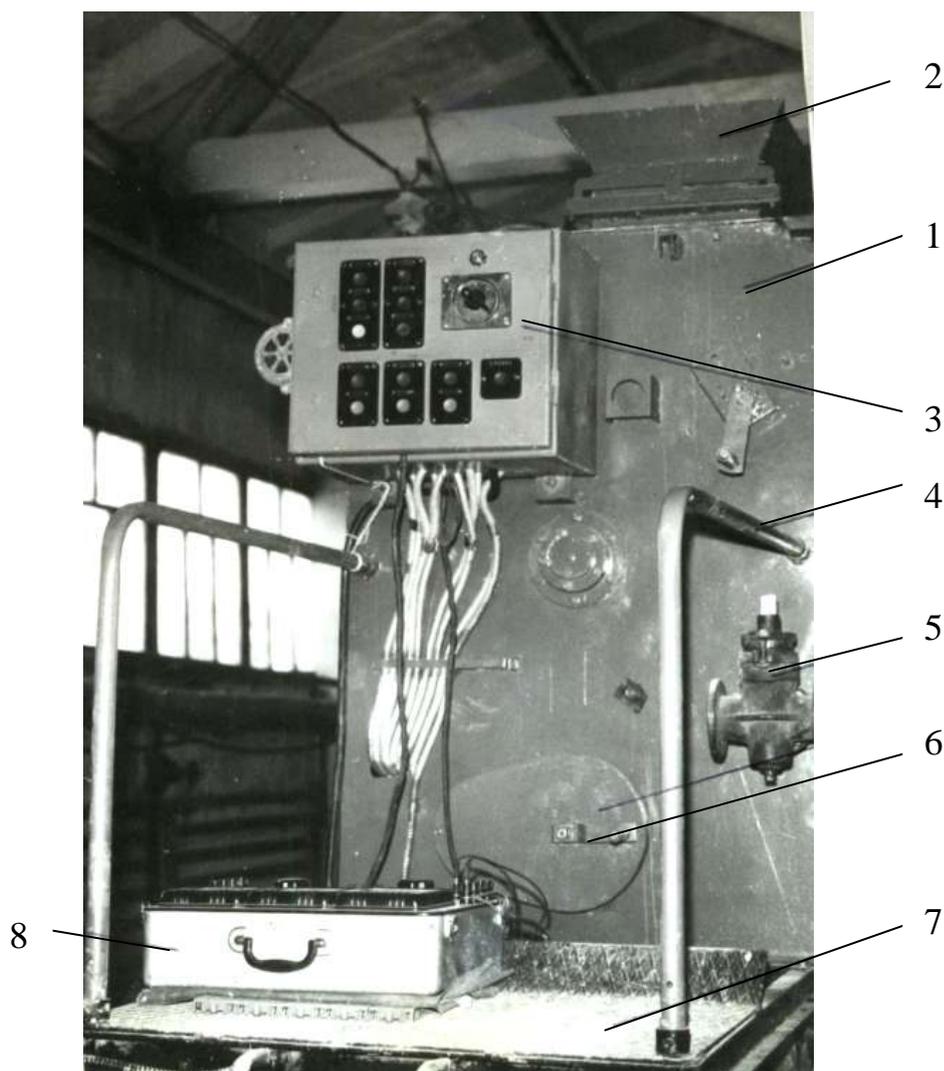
Общий вид агрегата (вид спереди):
